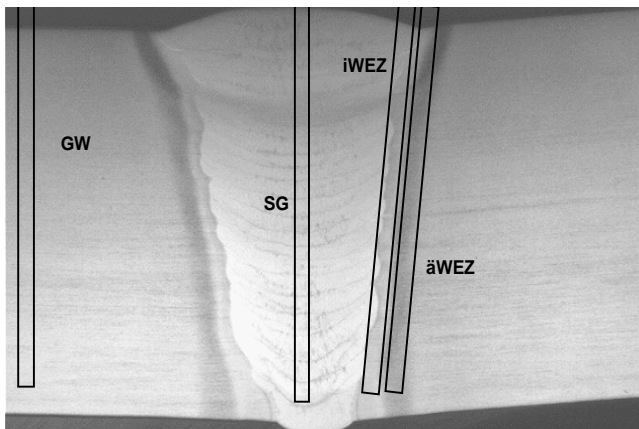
20 mm WIG-Engspalt-Schweißnaht mit schematisch angedeuteter Probenlage
